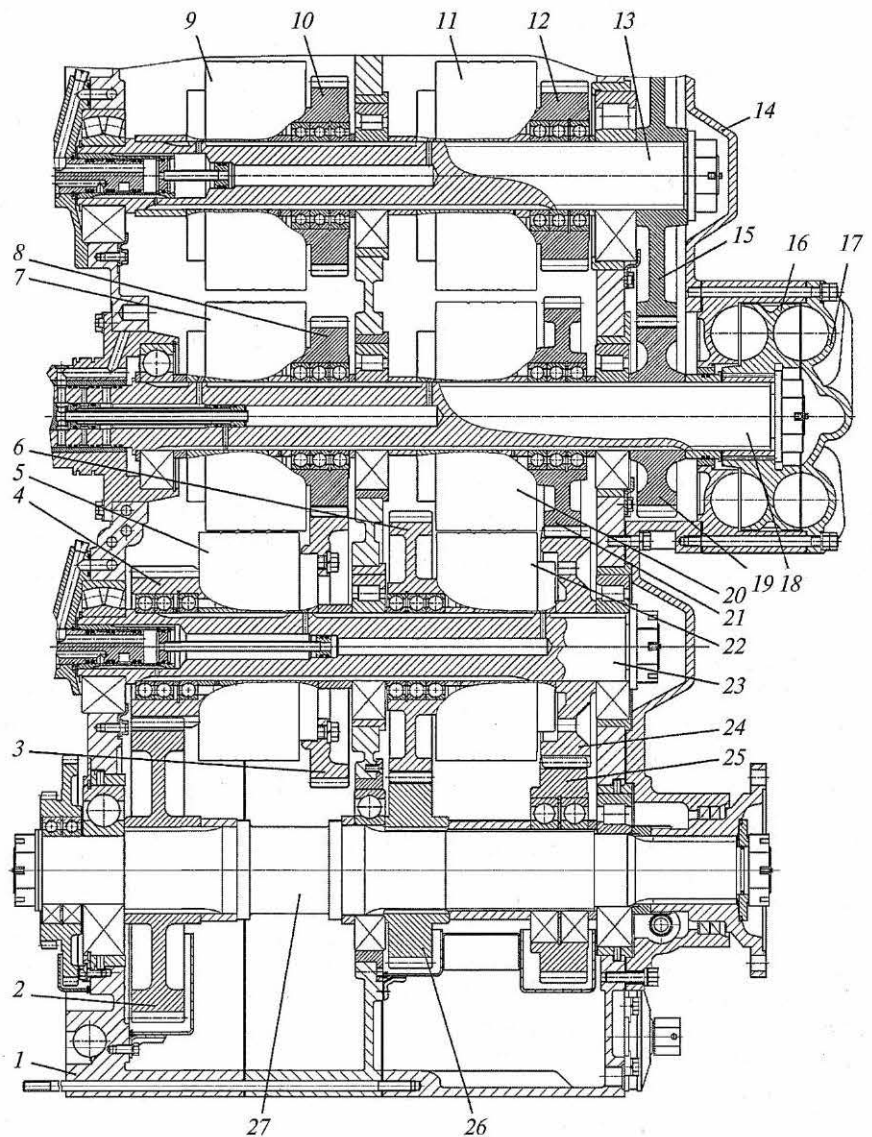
Коробка передач карьерного самосвала БелАЗ-7555Е:
